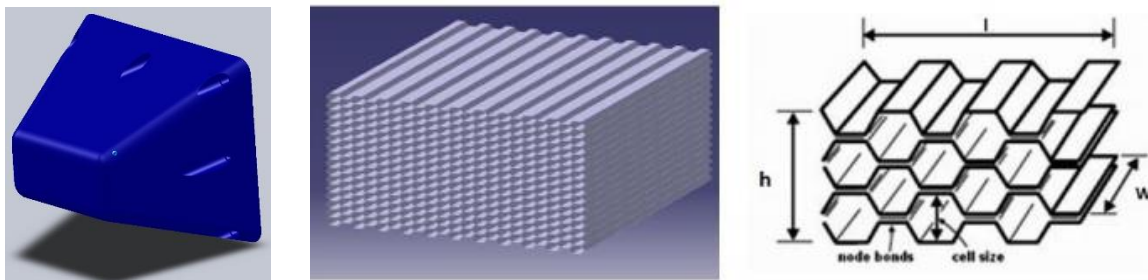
A la izquierda, arreglo en forma cónica, generalmente manufacturado en materiales compuestos o bajo trabajo en lámina [4.6]. A la derecha, arreglo en forma de honeycomb, generalmente manufacturado en aluminio [4.7].
